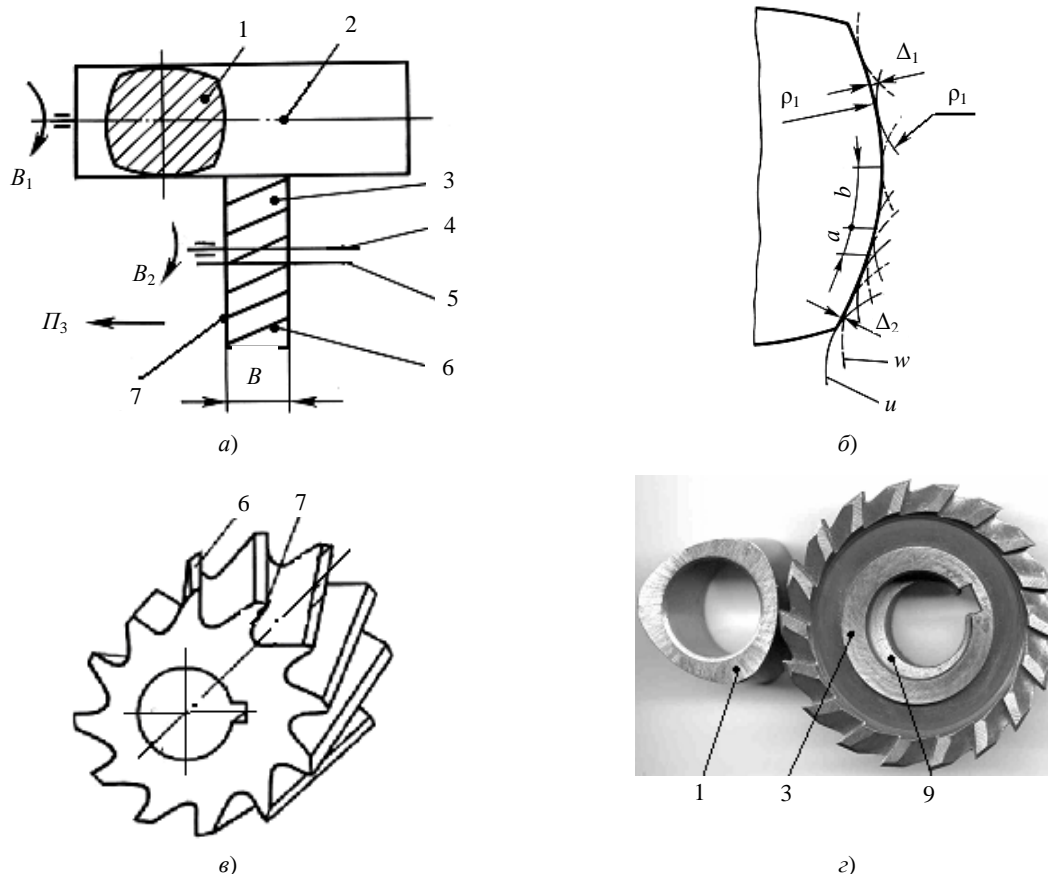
Кинематическая схема обработки некруглой поверхности (а), схема ее профилирования (б) методом касания, конструктивная схема режущего инструмента (в), образцы детали с некруглой поверхностью и режущего инструмента (г)
